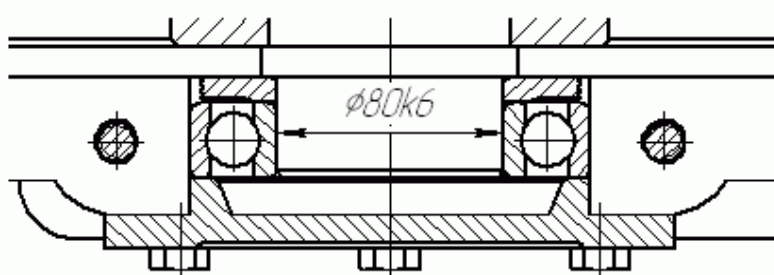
Размер с квалитетом ступени вала под подшипник
